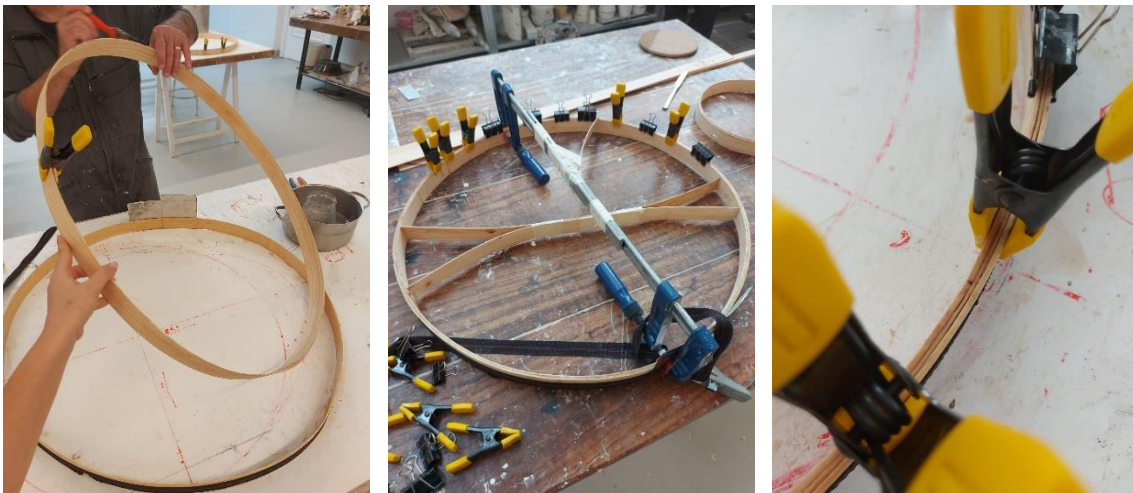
Conjunto de imagens do processo produtivo do molde circular em madeira.
